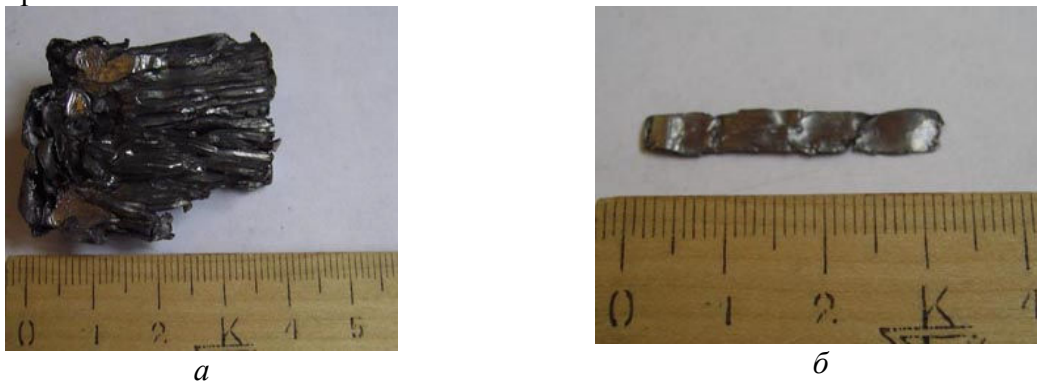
Образец полученный ИПД выдавливанием: а – образец в разрезе, б – деформация дробинки на поверхности образца.
